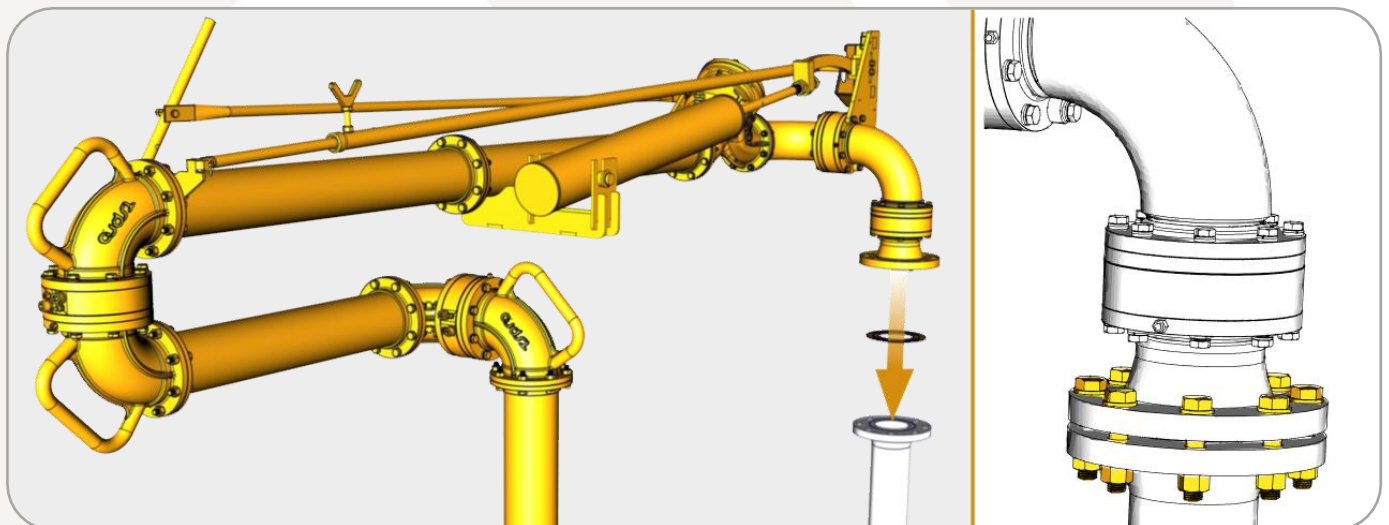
Fixação do Braço de Carregamento no Flange de Entrada
